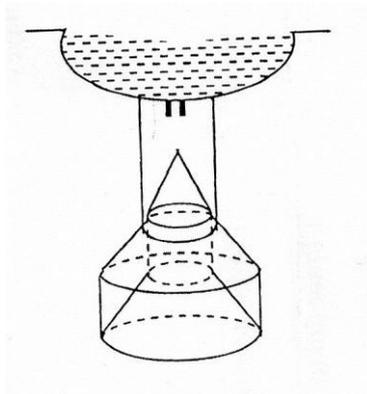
Изготовление кольцевой части сплава и схема присоединения кварцевой трубки к тиглю
